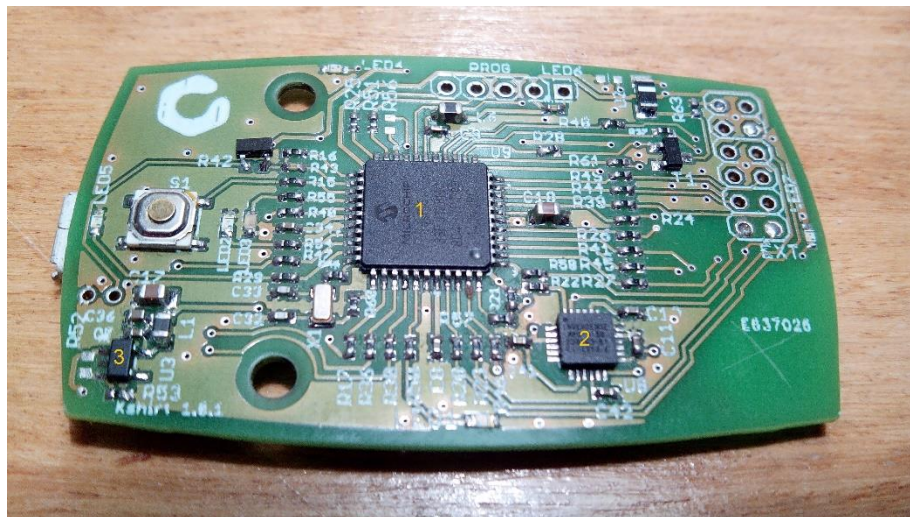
Frente da placa PCB da versão 1 do dispositivo Kshirt.
